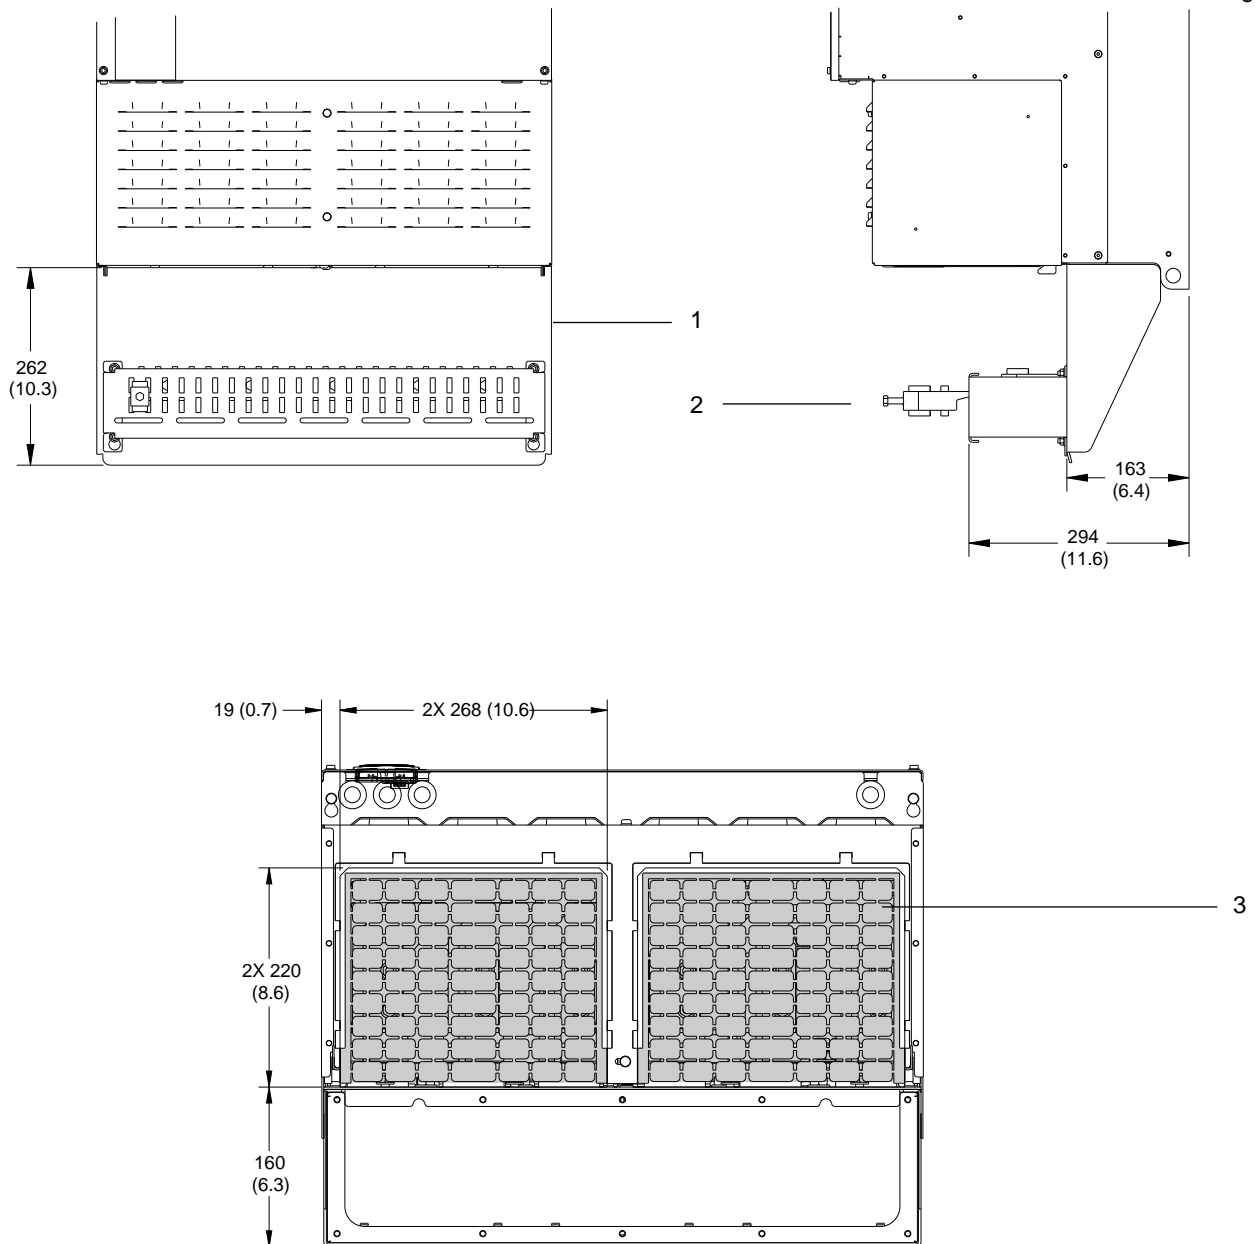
Terminaison du blindage RFI et dimensions de la plaque d'entrée des câbles pour E4h
